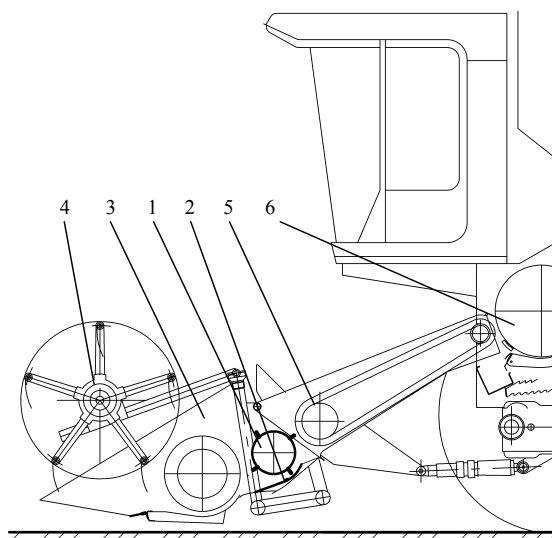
Схема загального вигляду жнивварки комбайна з пристроєм попереднього обмолоту зерна: 1 – зубчато-лопатевий молотильний барабан; 2 – дека; 3 – жнивварка; 4 – мотовило; 5 – транспортер похилої камери; 6 – МСС комбайна
